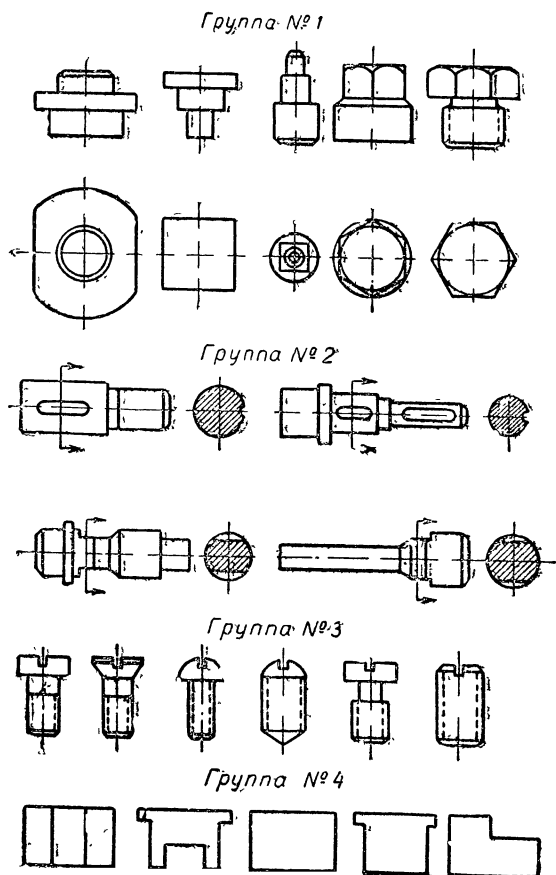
Детали, проходящие групповую обработку на фрезерных станках.
